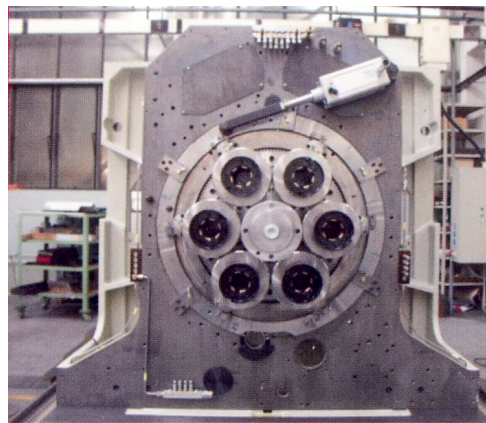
Manipulátor- odebrání hotových dílců [11]
